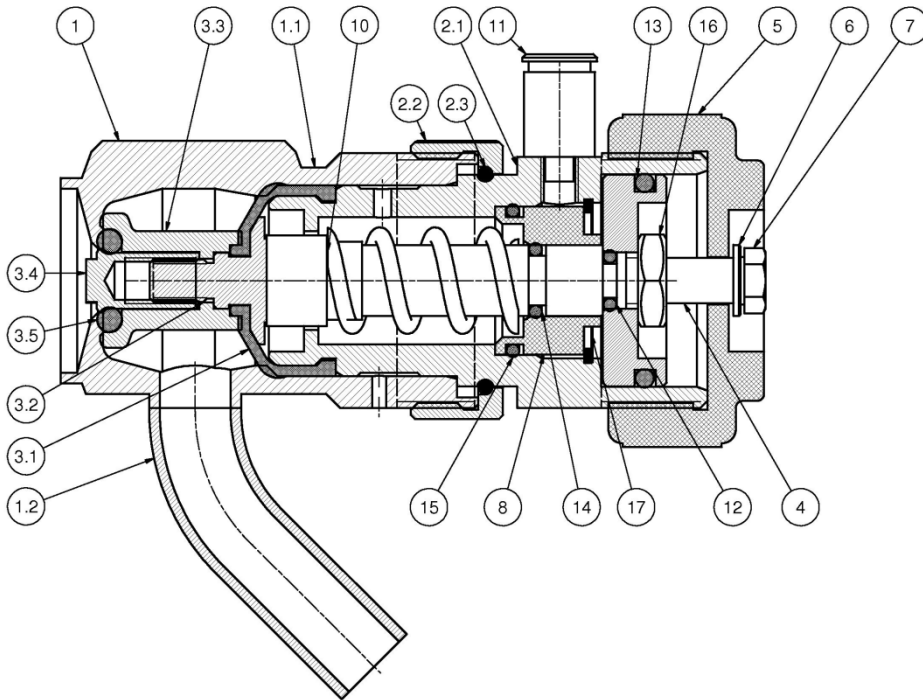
Schnitt PharmCom–Probenahmeventil manuell / pneumatisch ohne Spülanschluss
